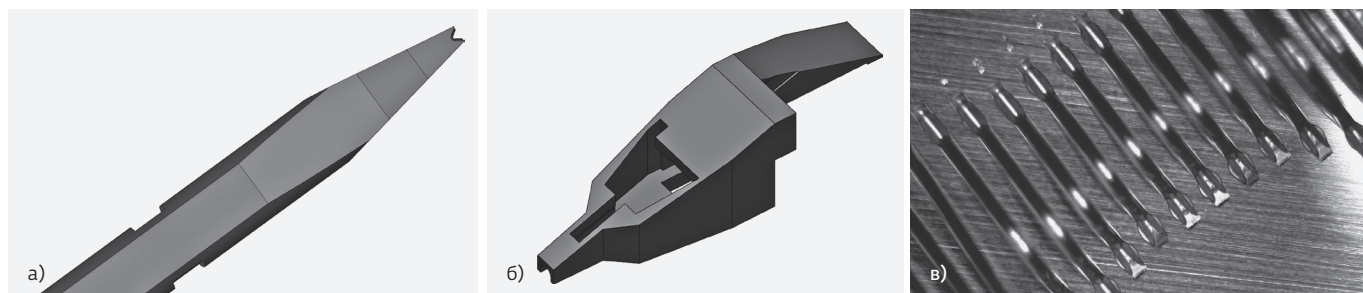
Сварка проводников повышенного сечения: а – рабочий торец сварочного инструмента; б – пластиковая направляющая для проволоки; в – получаемое соединение
